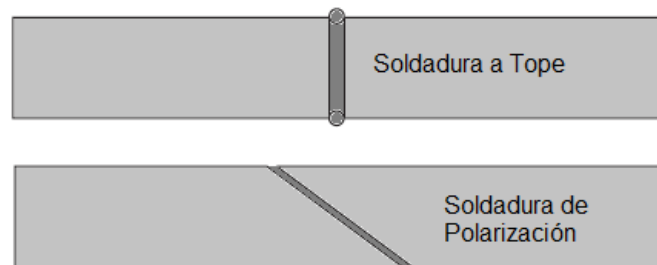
Soldadura longitudinal y de polarización
